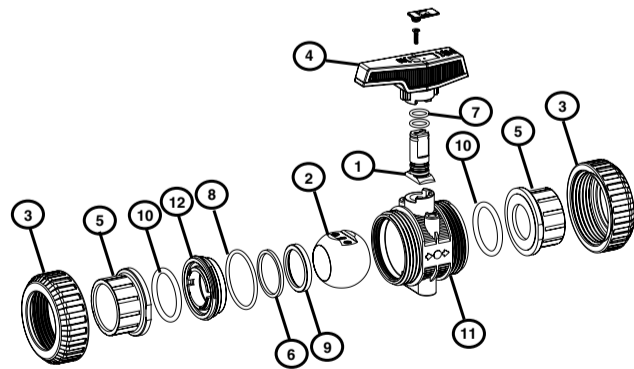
FIG.	Parts	Pièces	Despiece	Parti	Bautelle	Peças	Material
